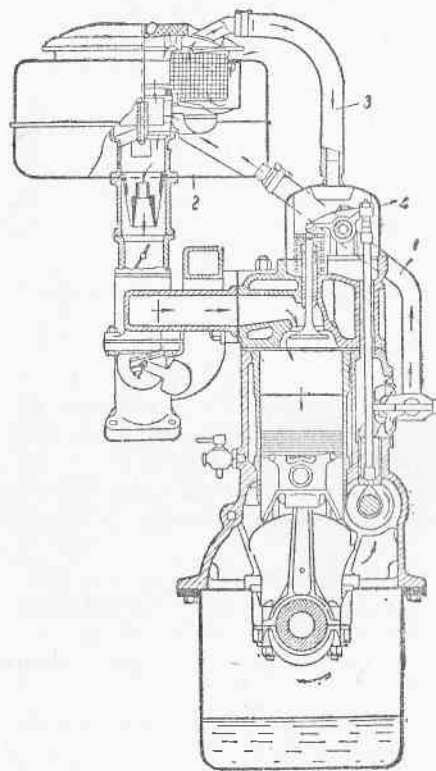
Схема вентиляции картера двигателя автомобиля М-21 «Волга».
